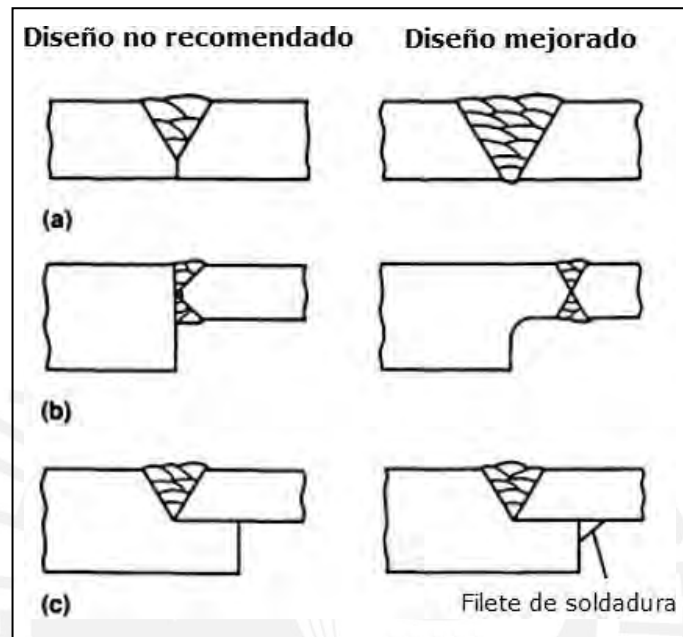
Modificación de mejora en uniones soldadas [3].
